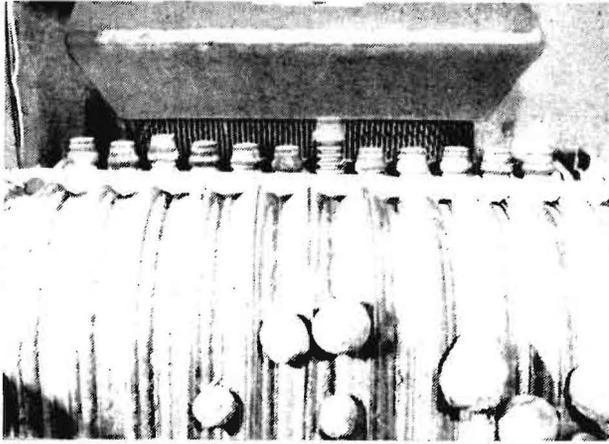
Eingebaute Trennmechanismen in der E 961 (Draufsicht)
